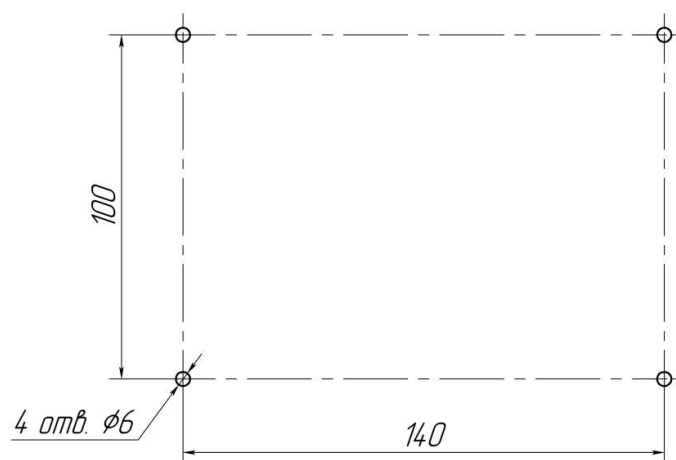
Габаритные и установочные размеры ВП (металлический корпус)
